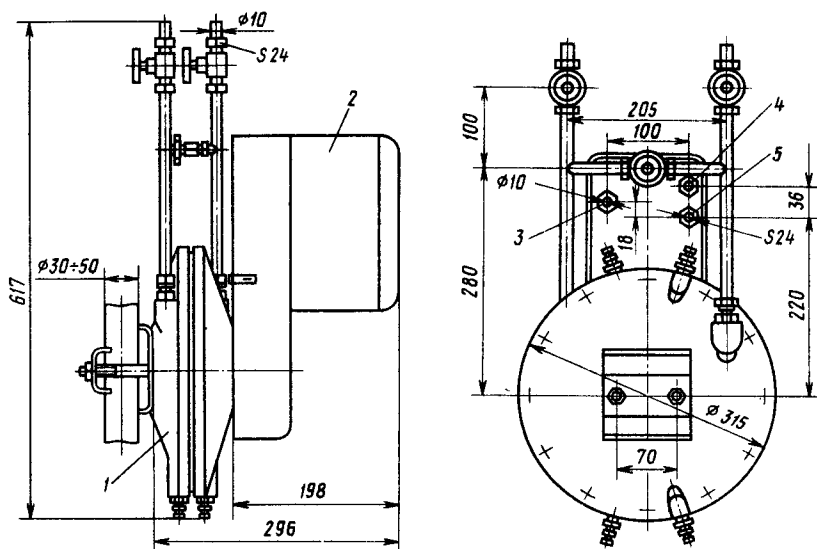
Общий вид и габаритные размеры датчика ДРДРГ-100:
